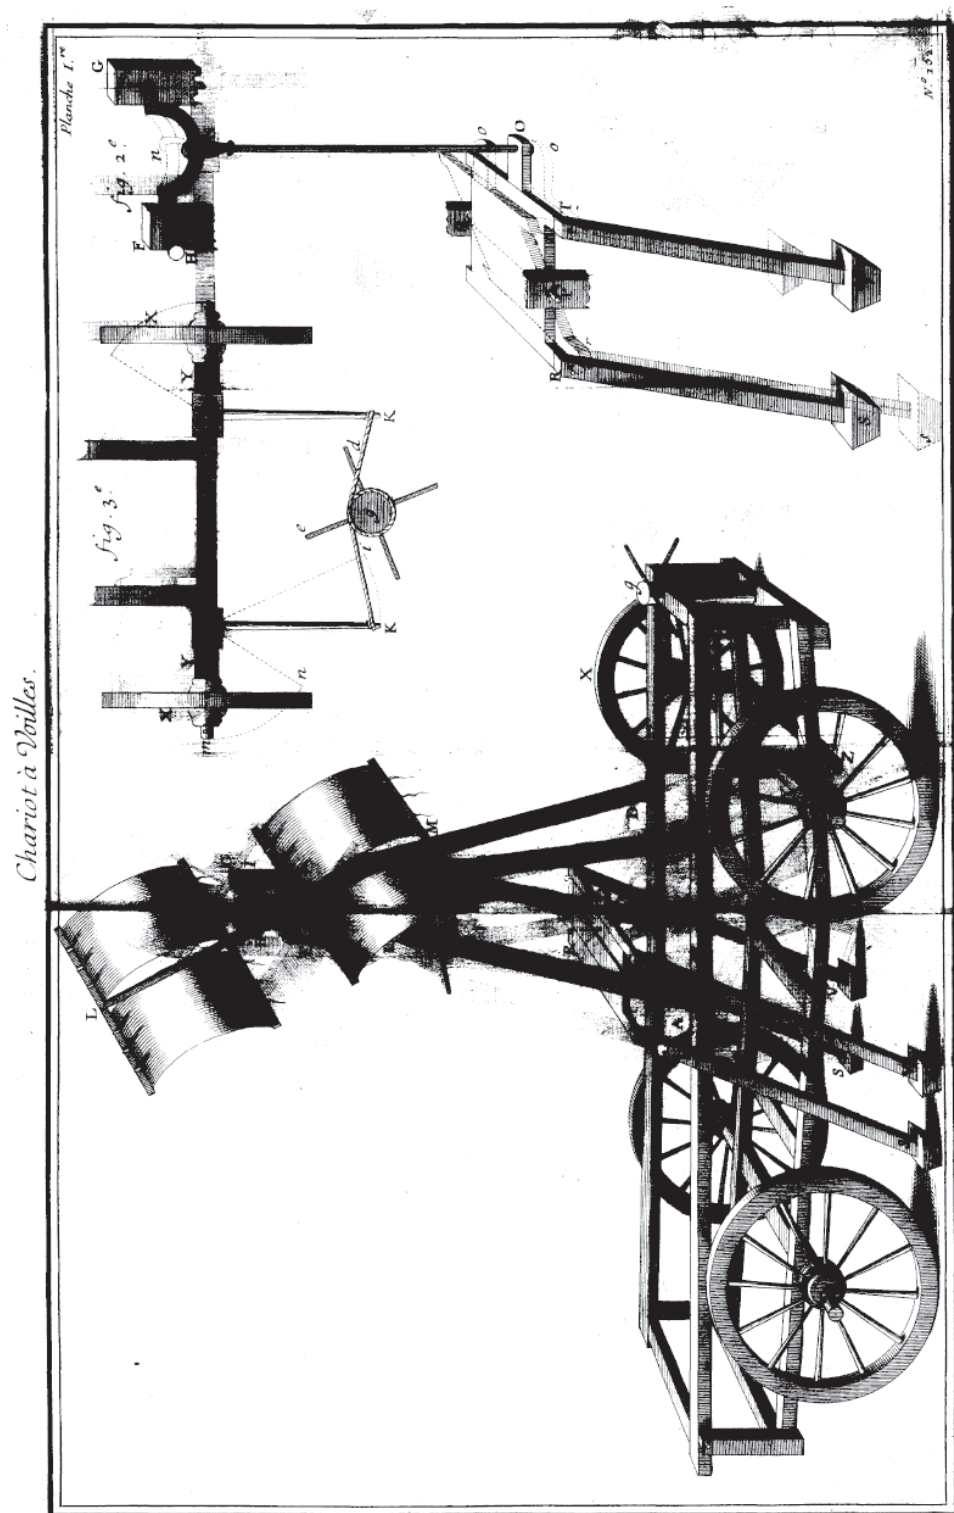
Premier chariot à voiles de Du Quet, approuvé en 1714 à l'Académie (figure tiré du tome III des Machines, p. 36)
